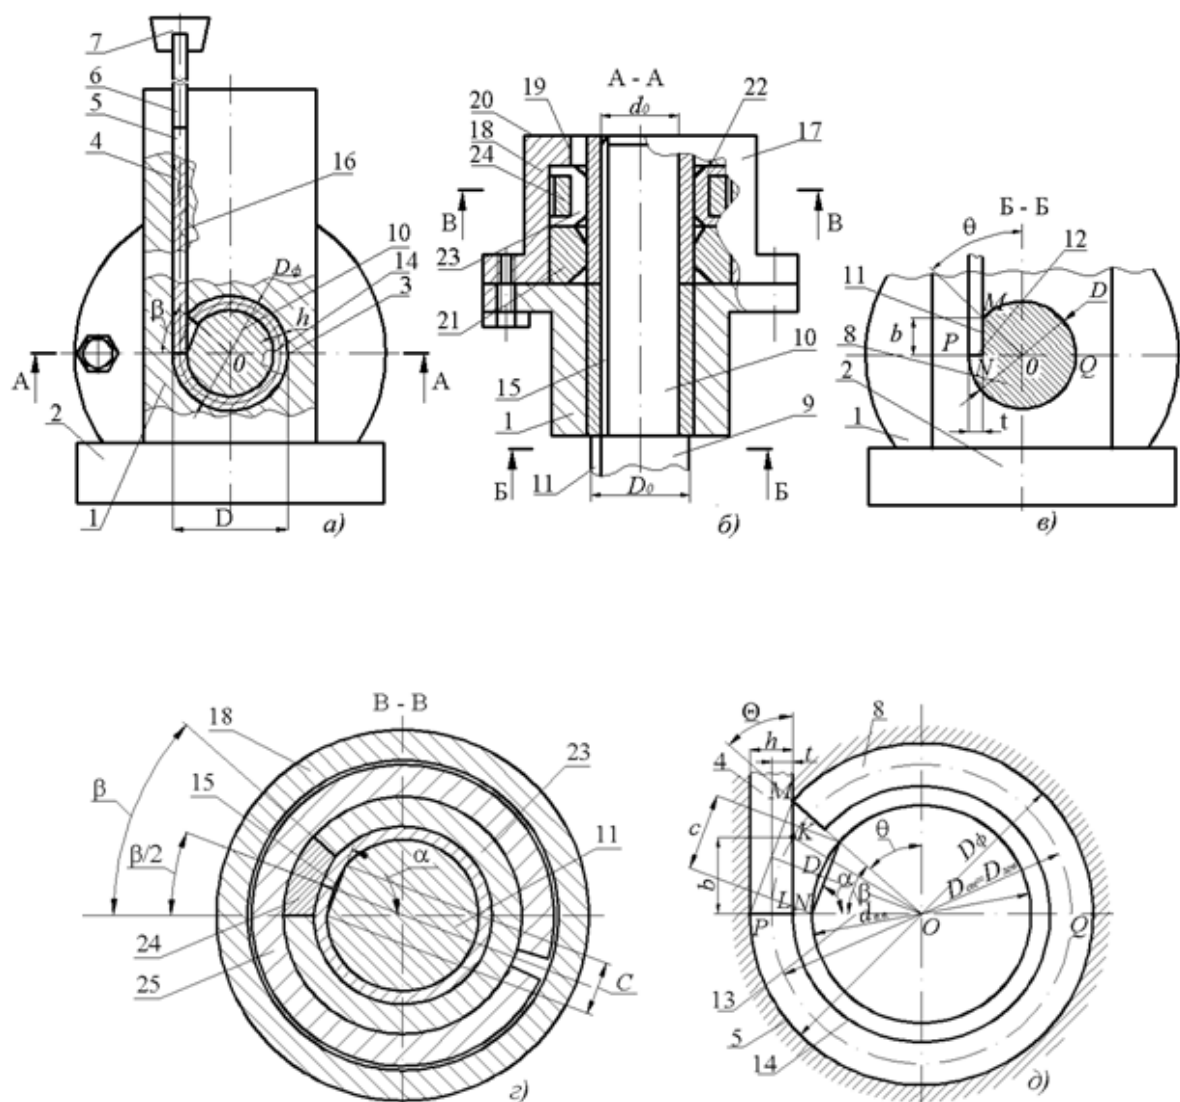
Пристрій для формування і калібрування згортних втулок:
